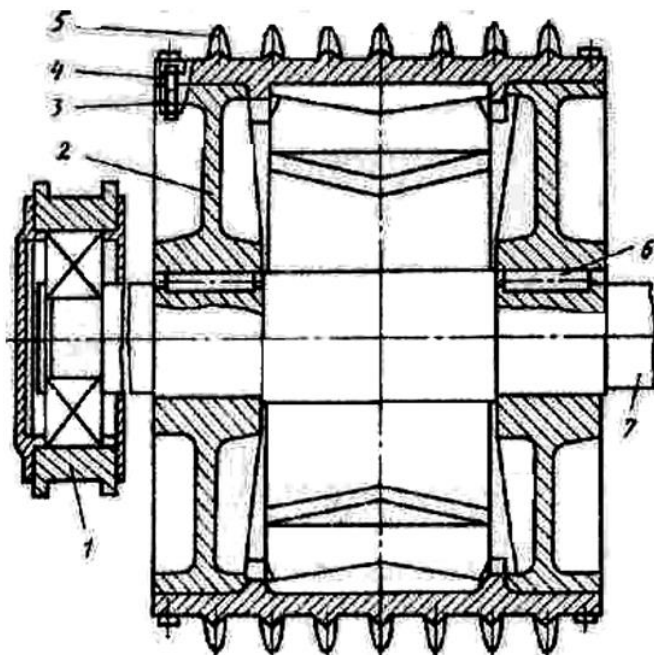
Валок двовалкової зубчастої дробарки СМД – 175А:
